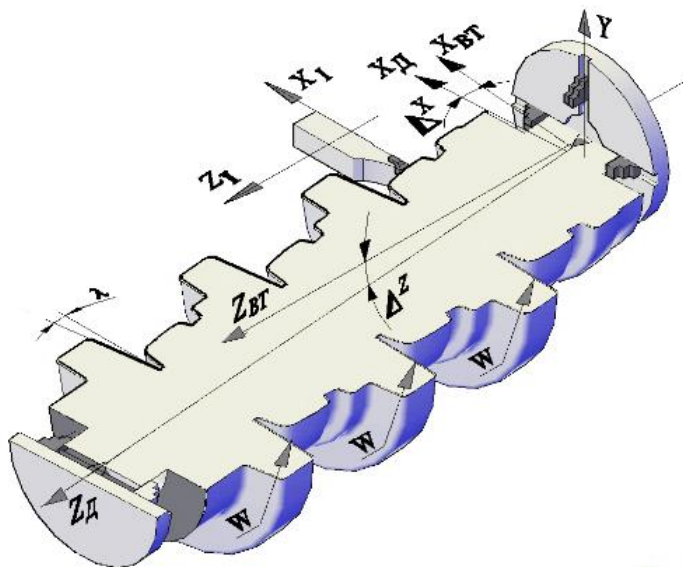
Базування валка у центрах на вальцетокарному верстаті з ЧПК.
